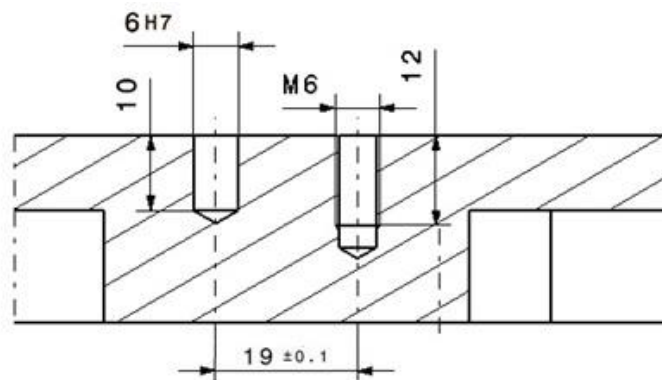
Detalhe dos furos de fixação do molde [18]
